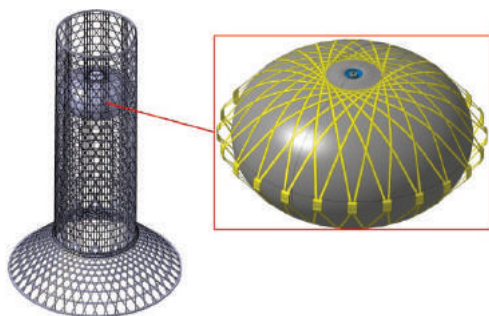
Размещение бака внутри силовой конструкции корпуса КА
